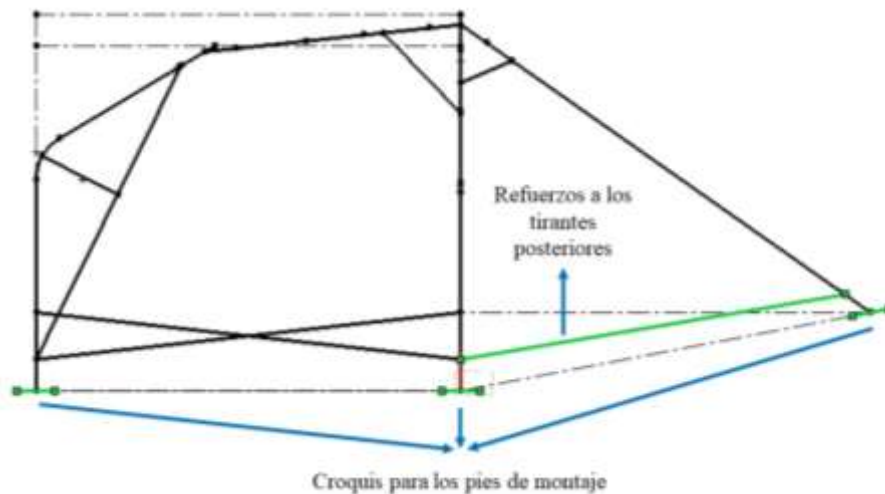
Tirantes de refuerzo para los tirantes posteriores. Pies de anclaje
